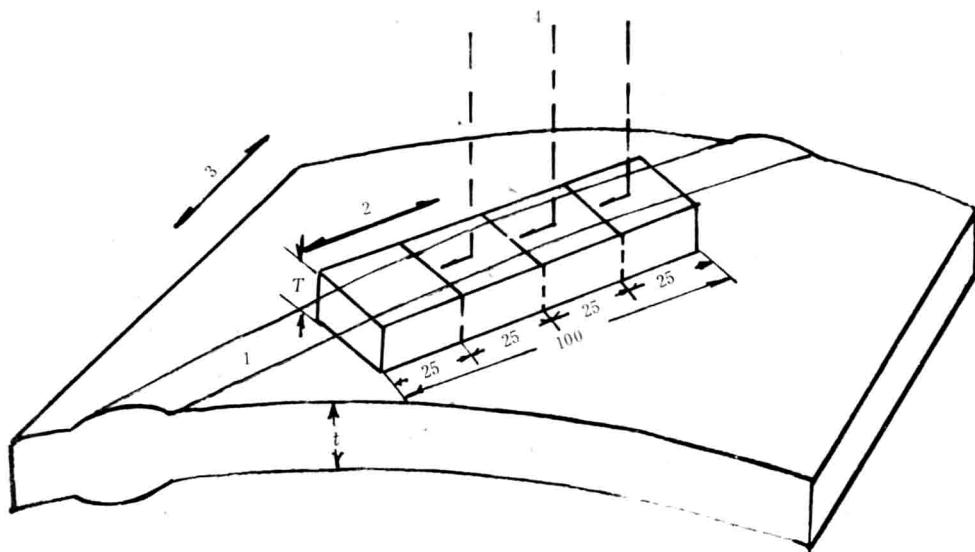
螺旋焊管纵向焊缝试样取样部位
